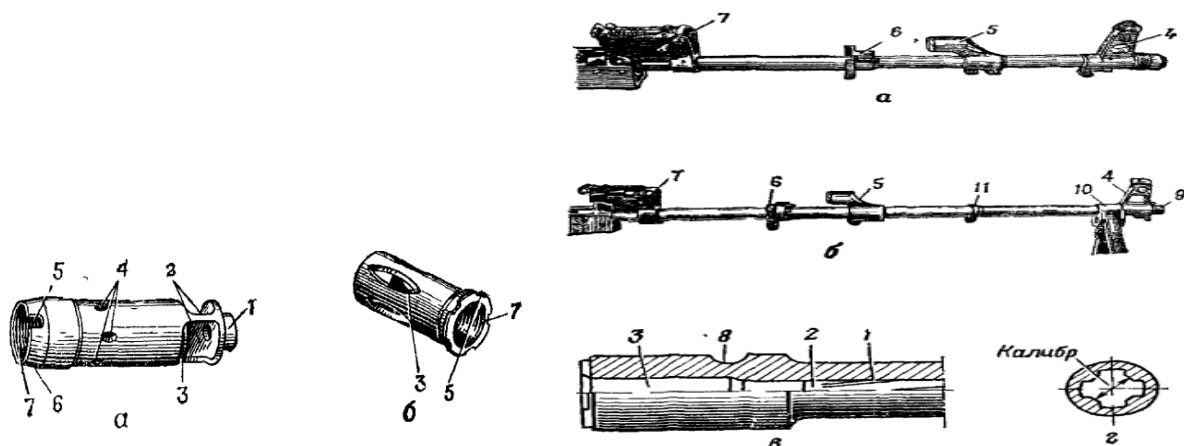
Дульный тормоз-компенсатор и пламегаситель:
